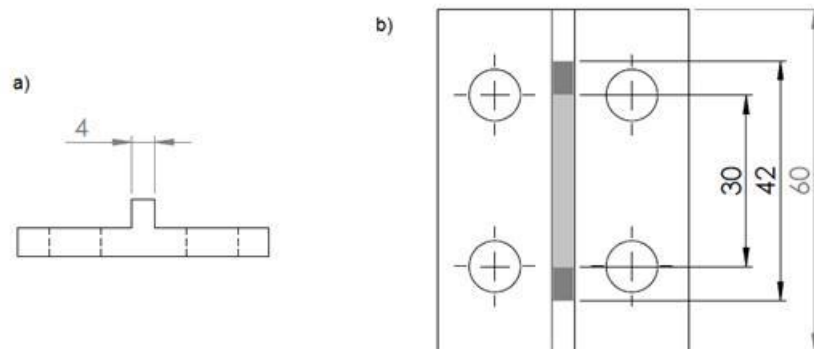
Base del espécimen de compresión. a) vista de planta, y b) vista superior. El sombreado claro indica el área cuando el espécimen no se ha deformado. El sombreado oscuro indica el área del espécimen a máxima deformación
